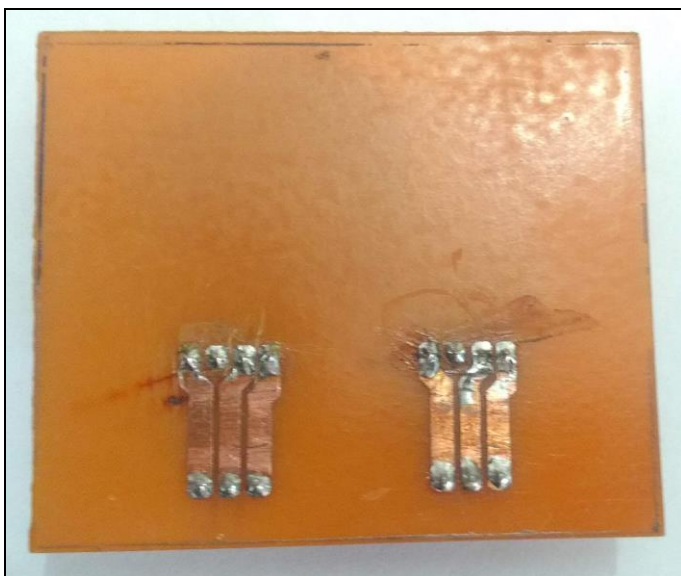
PCB da base dos sensores após o processo de corrosão.
